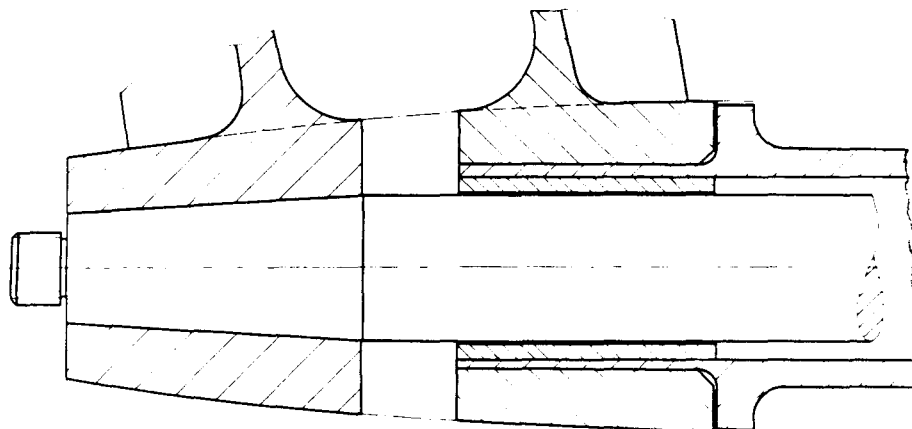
Befestigung von gegenläufigen Propellern; hinterer Propeller nach dem paßfederlosen SKF-Öldruck-Schrumpfsitz-Verfahren, vorderer Propeller mittels Wellenflansch befestigt.
